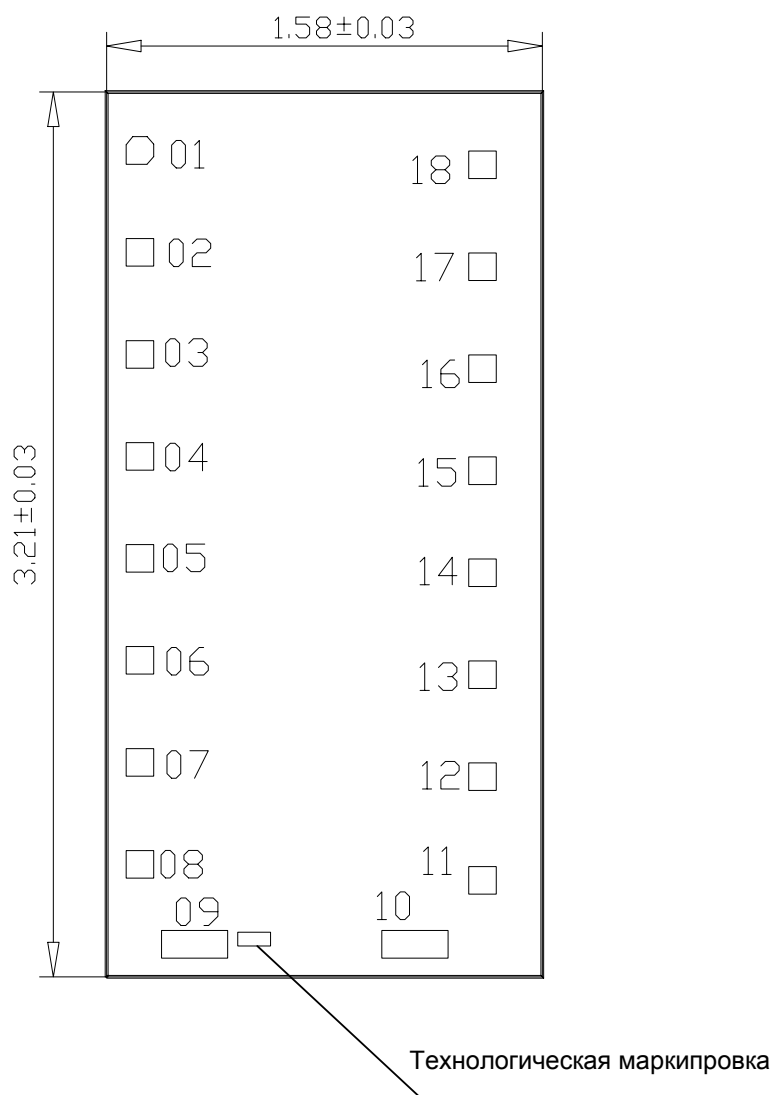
Габаритный чертеж корпуса MS-001AC
